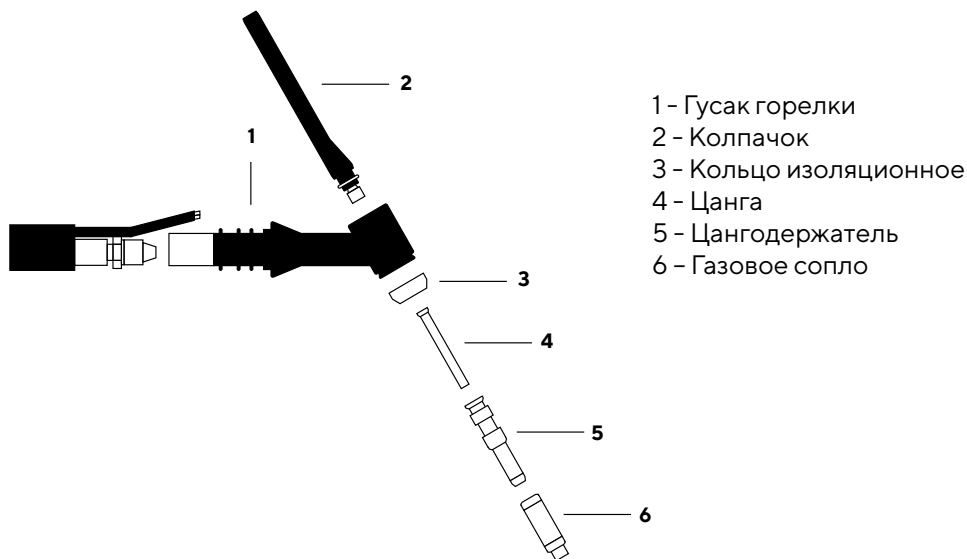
Составные части горелки для TIG сварки
